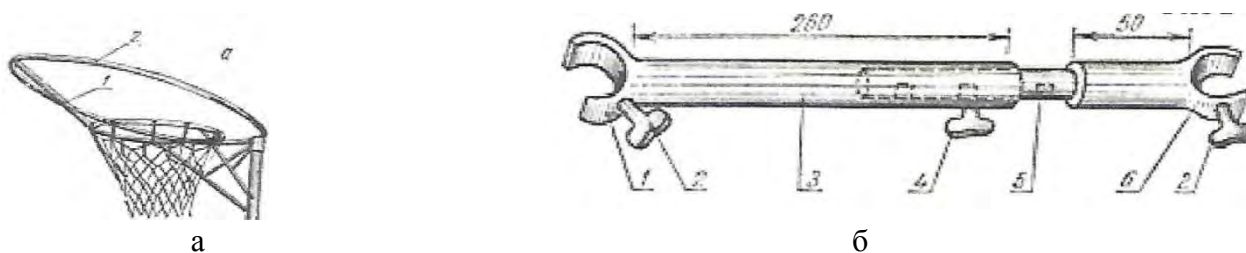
Устройство для совершенствования бросков в баскетболе
